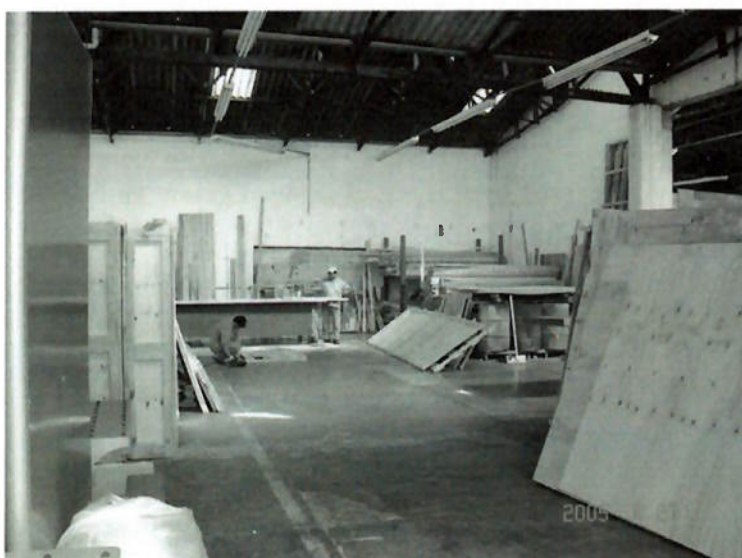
Expedição - área de armazenamento de madeiras e de execução de embalagens
